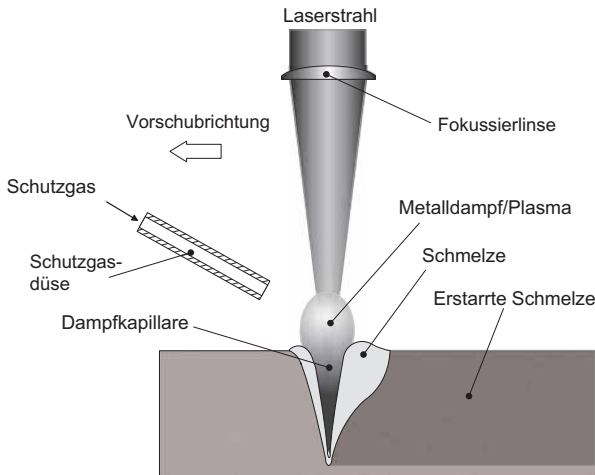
Zum Prinzip des Laserstrahltiefschweißens.
